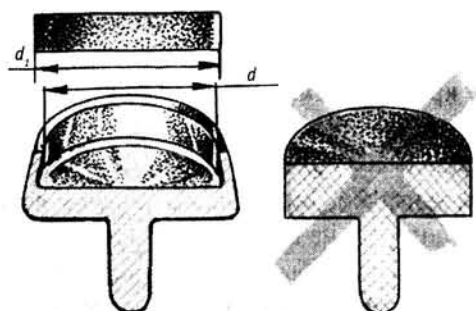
1—3. Детализовка вентильной головки с вращательно-поступательным движением штока:
